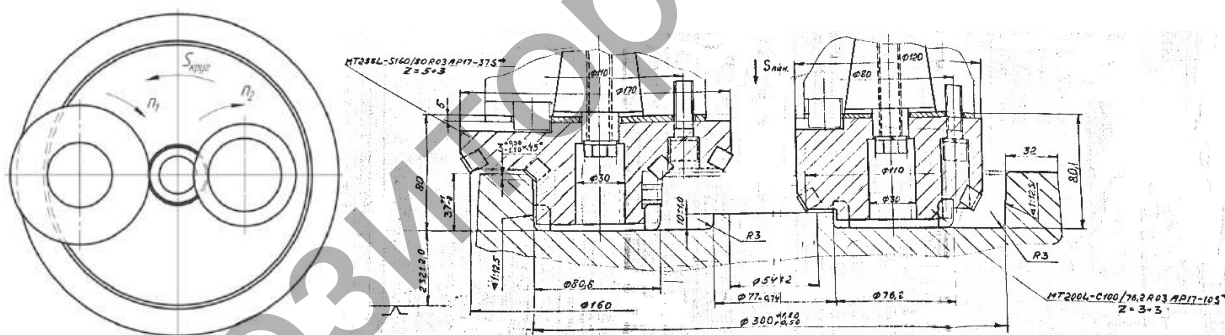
Эскиз детали, подлежащей обработке круговым фрезерованием
